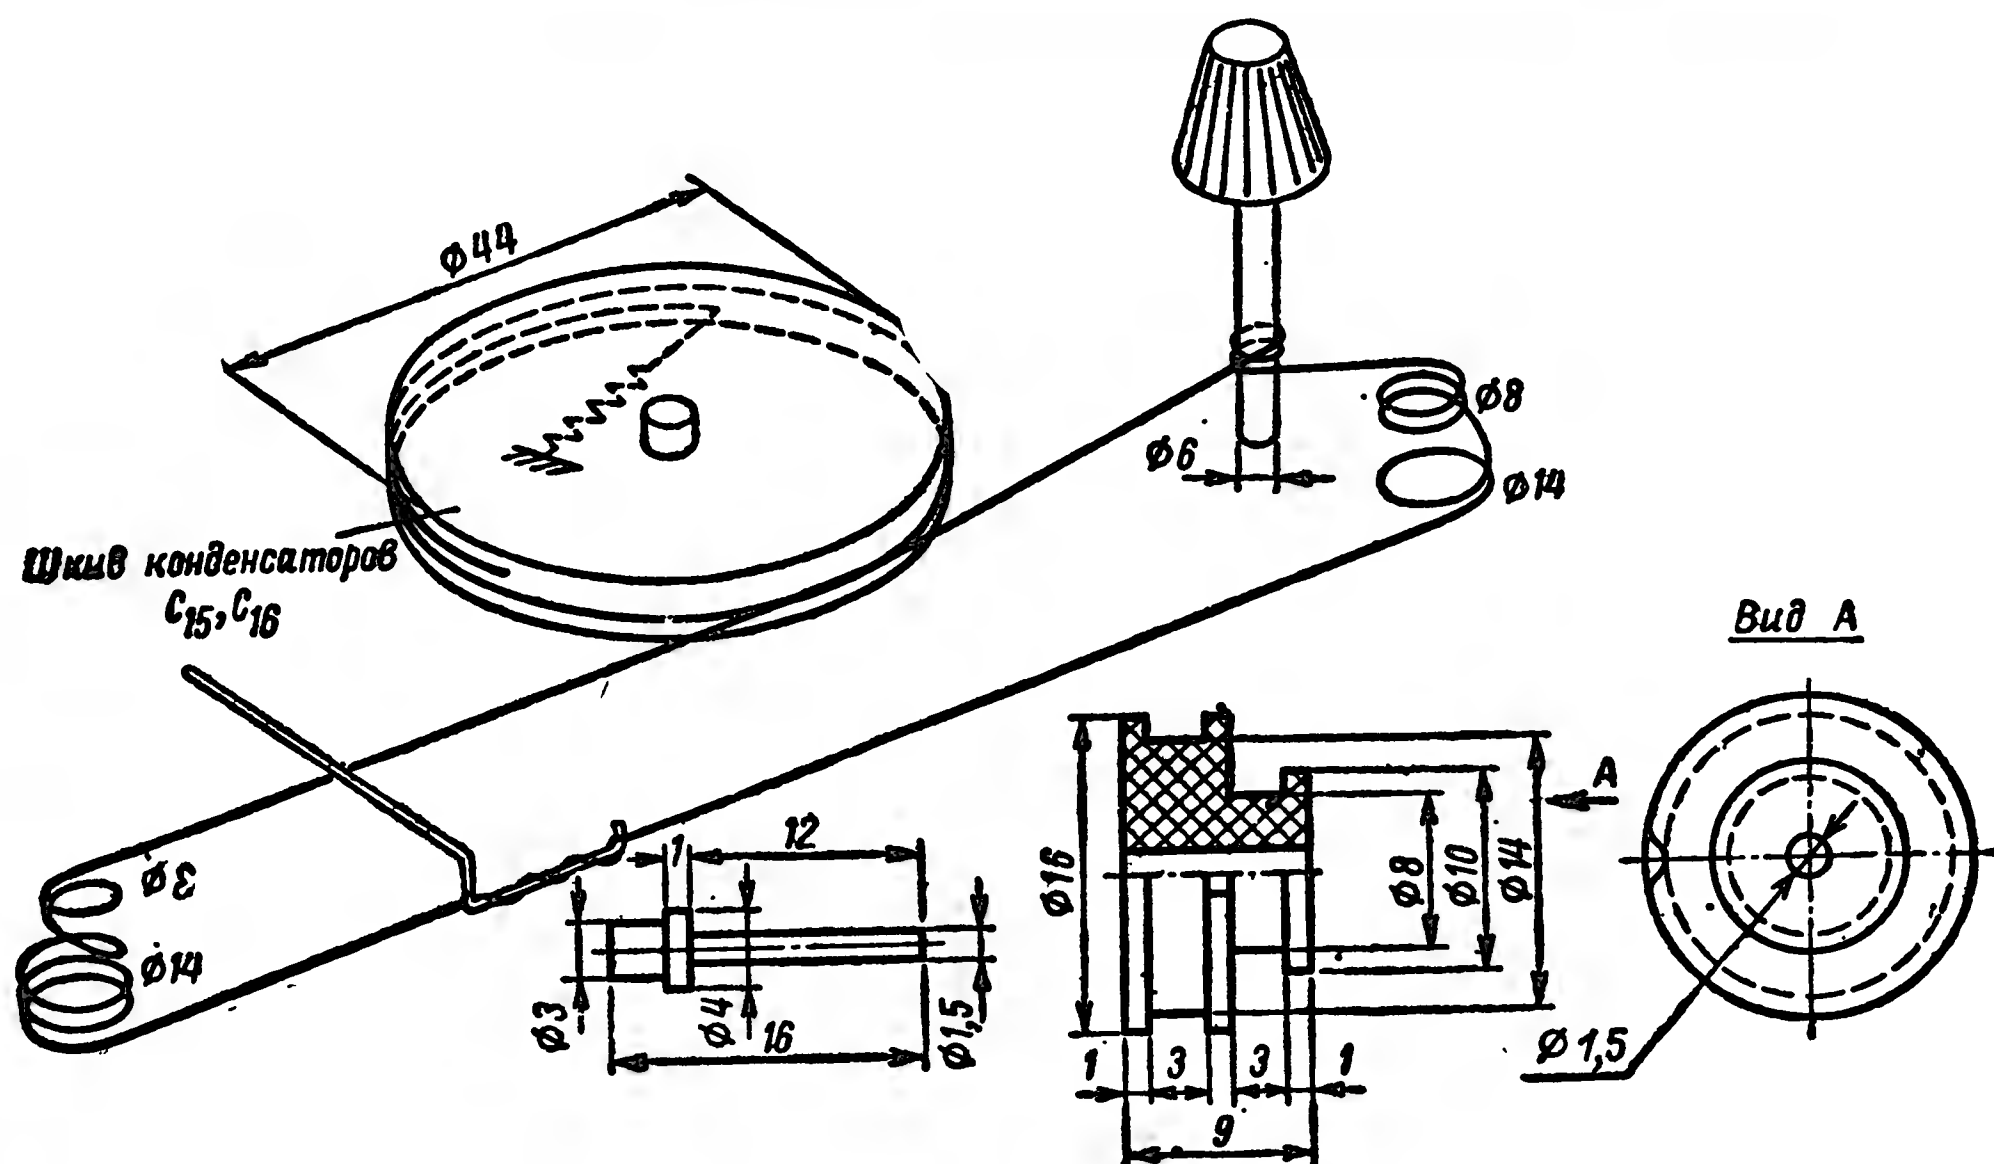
Кинематическая схема и детали шкально-верньерного механизма.
